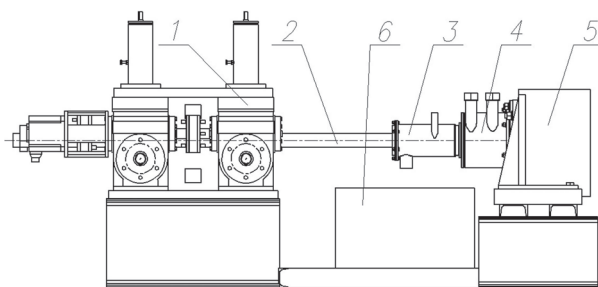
Схема установки непрерывного горизонтального литья: 1 – тянущее устройство; 2 – слиток непрерывный; 3 – вторичное охлаждение; 4 – кристаллизатор; 5 – металлоприемник; 6 – бак промежуточный
